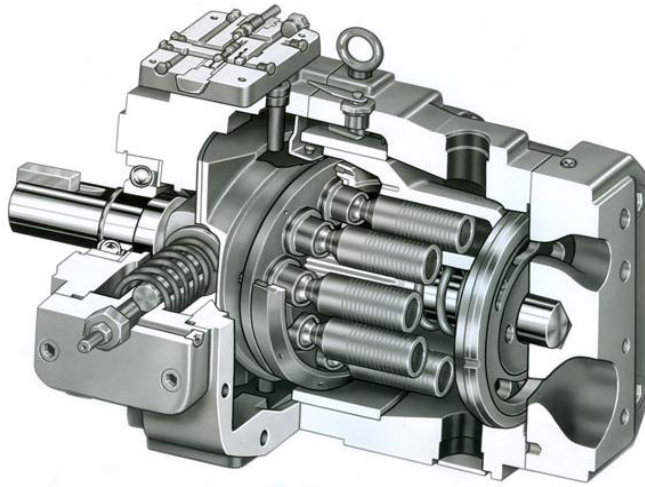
Bomba de pistón axial (<http://www.coha.com.co>)
